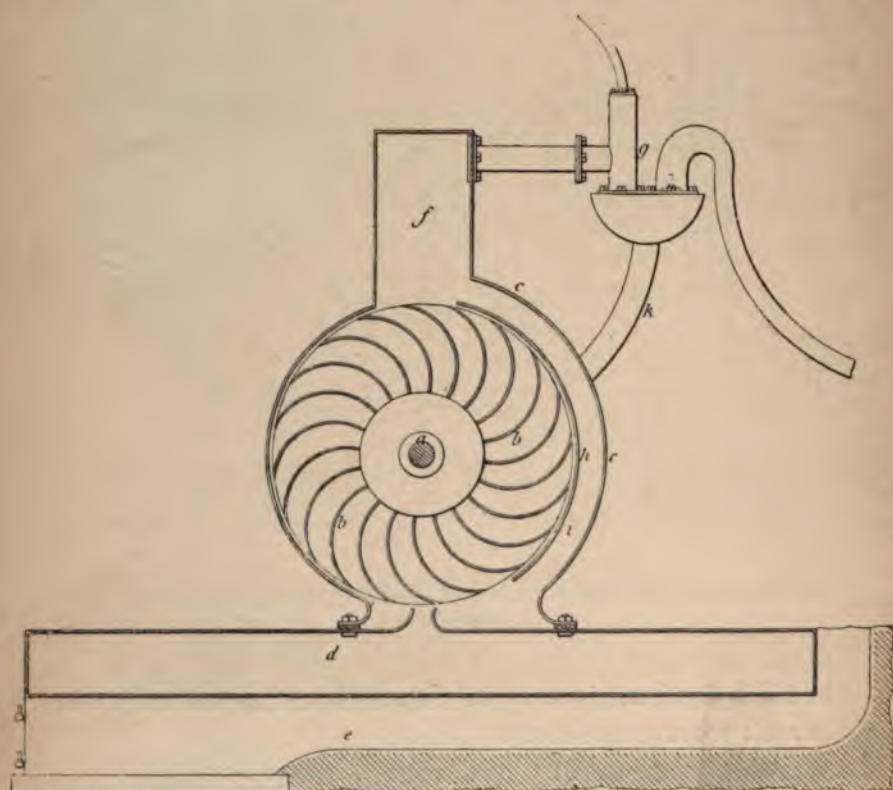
Roue à vapeur Dietz (1821). Vue d'ensemble du moteur et du générateur.
